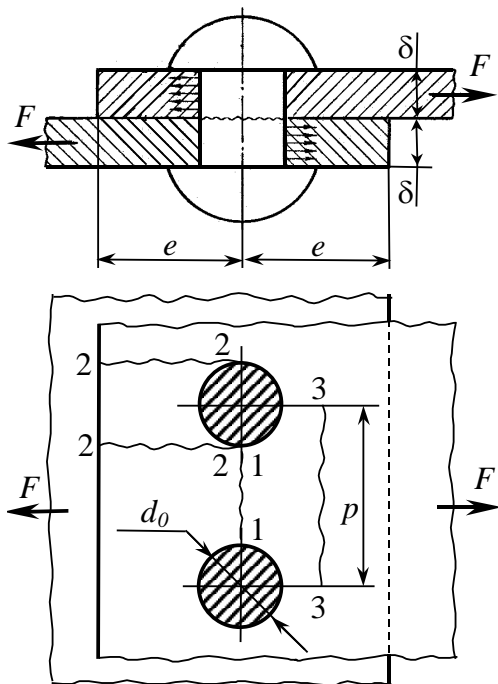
Розрахункова схема заклепкового з'єднання
